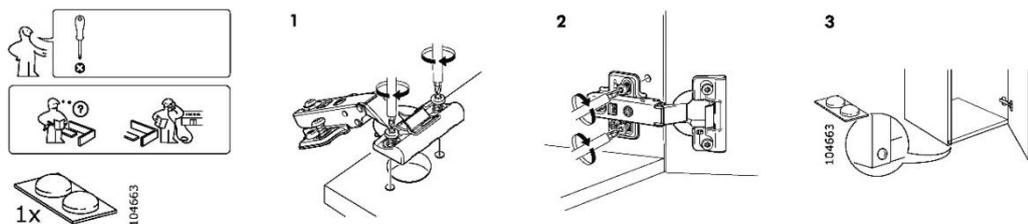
INSTRUCCIONES DE MONTAJE IKEA II
